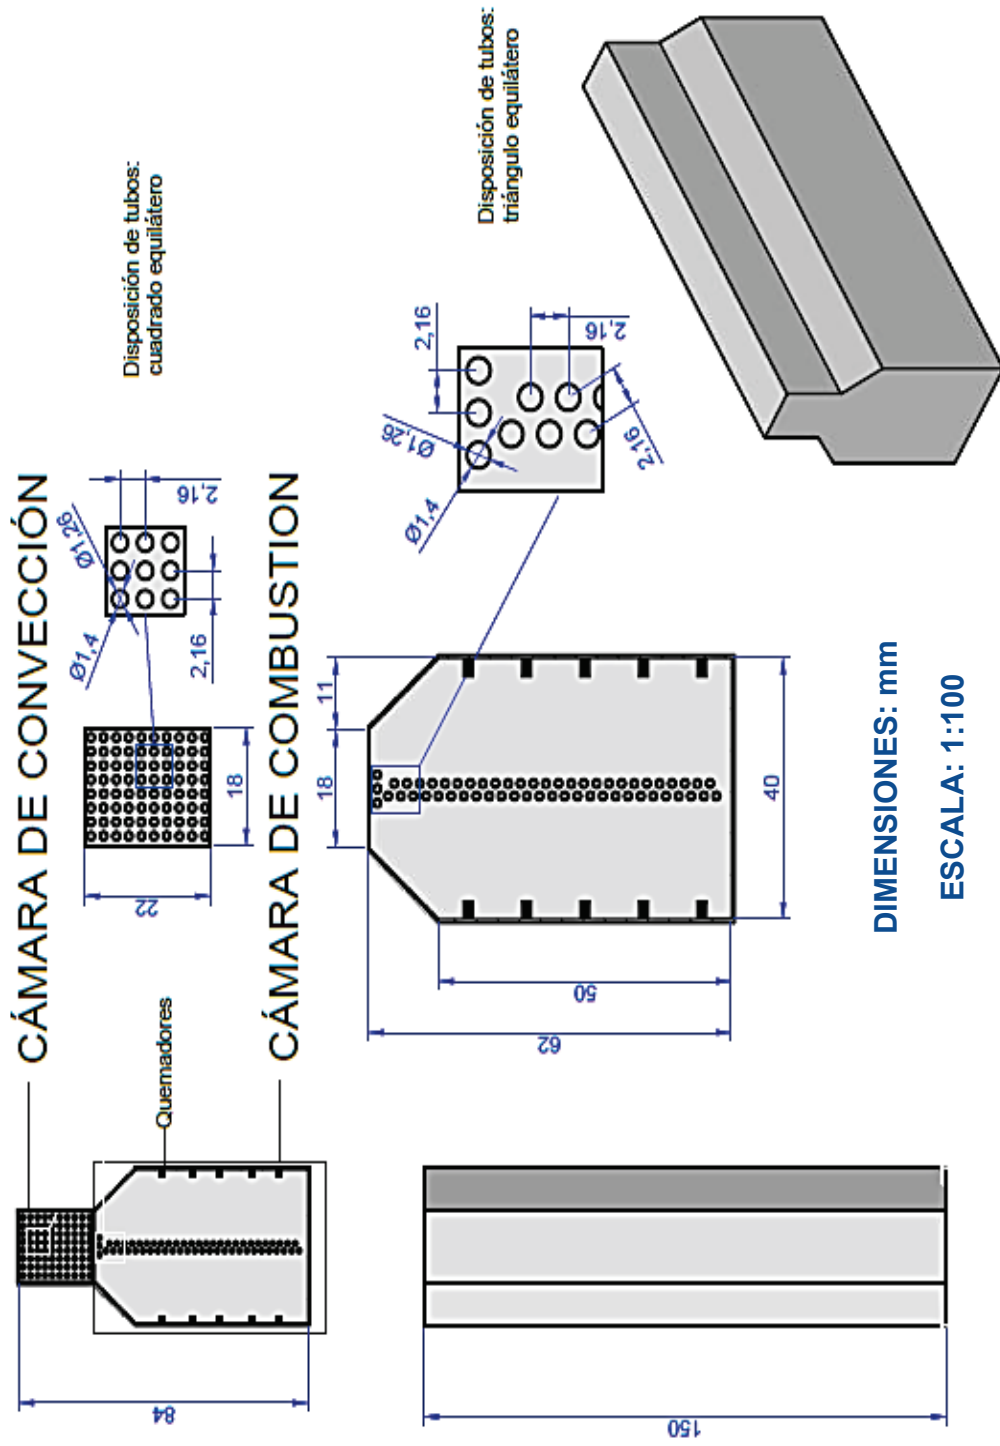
Dimensiones del horno tubular para el craqueo térmico (H-101/H-102)
